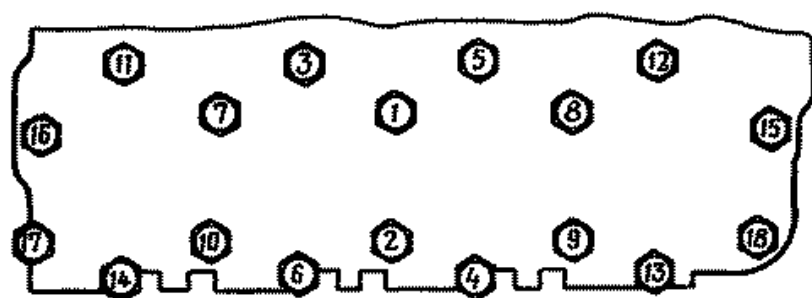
Последовательность затяжки гаек крепления головок блока цилиндров
